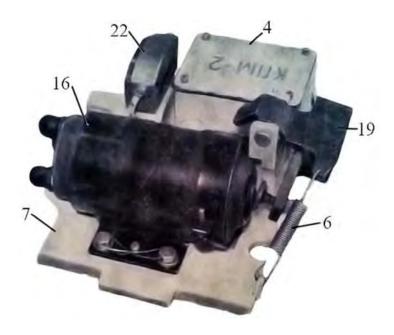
Общий вид спускового механизма: 4 – соединительный блок; 6 – пружина нажима; 7 – основание; 16 – электромагнит ЭМ-1Г (Y); 19 – полка в сборе; 22 – контактная пластина
